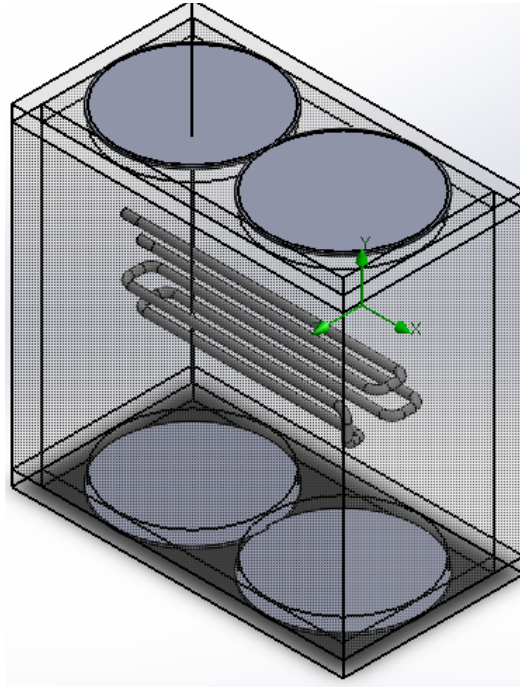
Ensamble de la caja y tubería, vista isométrica.
